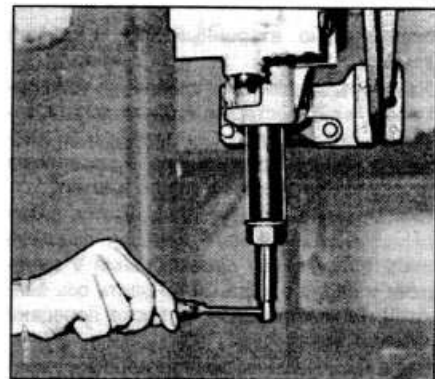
Установка вторичного вала в заднюю крышку коробки передач с помощью приспособления 16.042
